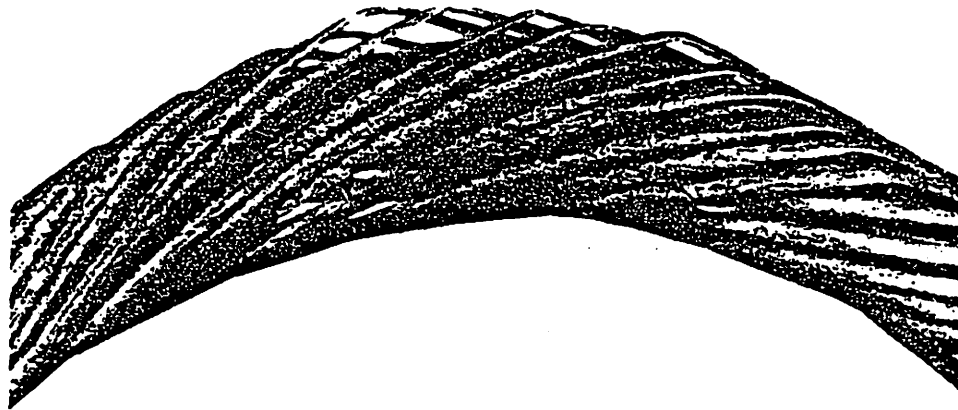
Drahtseil mit durch Korrosion und Abrieb gelockerten Drähten
